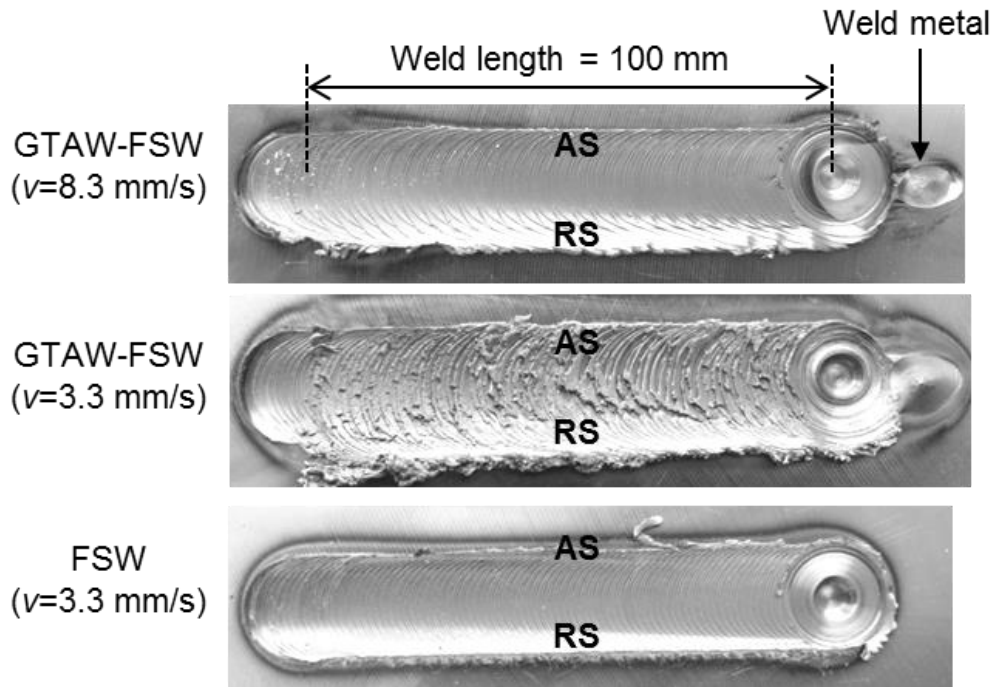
GTAW-FSW および FSW の接合部表面の外観写真
